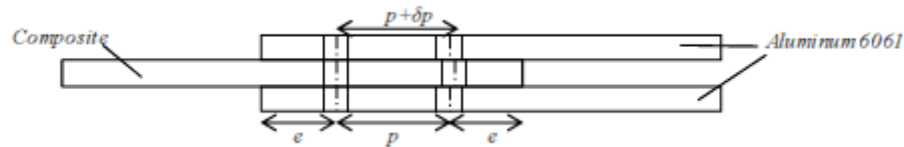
DimensionS de l'assemblage métal-composite double recouvrement avec défaut
